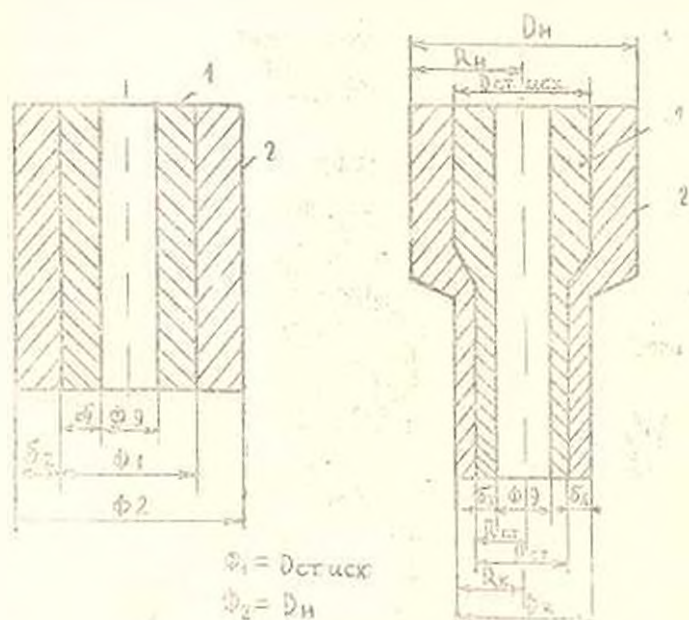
Схематическое изображение биметаллической заготовки ПЖ4М—БрОЦС 5-5-5: а — до экструзии, б — в процессе экструзии; 1 — втулка, 2 — стержень.
